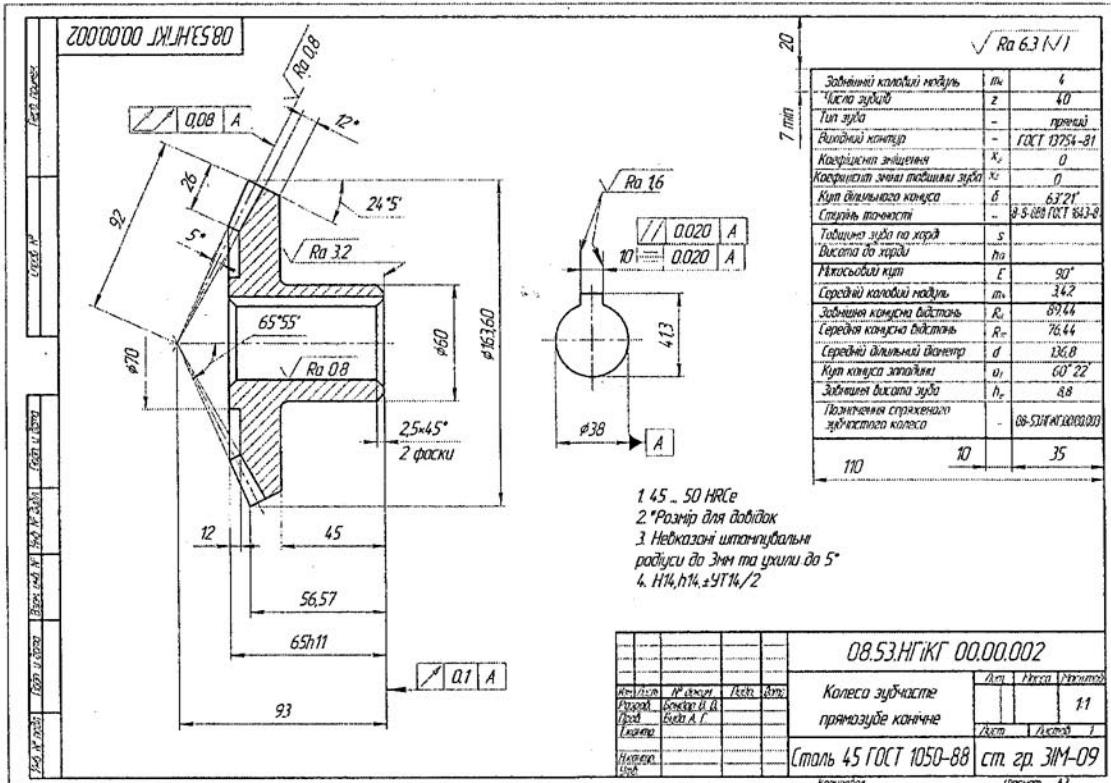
Робочий кресленик прямозубого конічного зубчастого колеса
